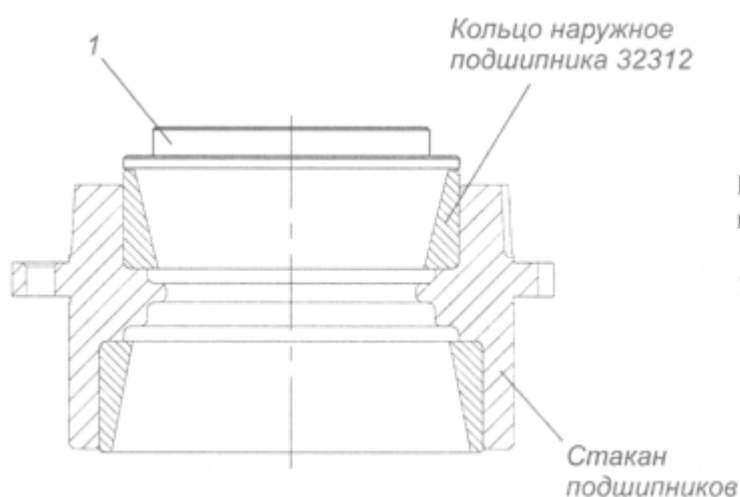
Запрессовка наружного кольца подшипника 32312:
